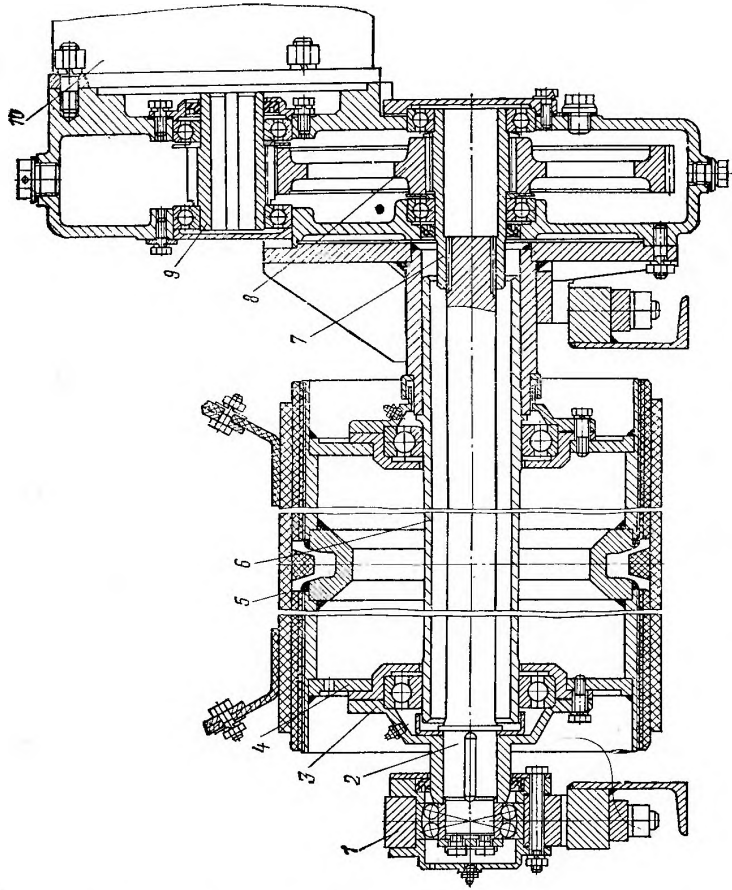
Редуктор привода транспортера экскаватора ЭТР231
